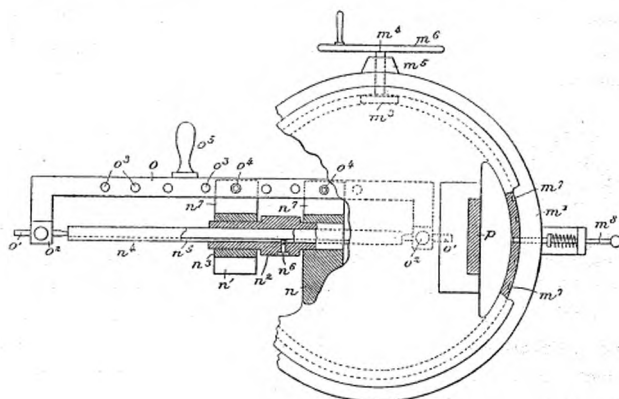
Coupe en plan suivant 4, 4 (fig. 102).
